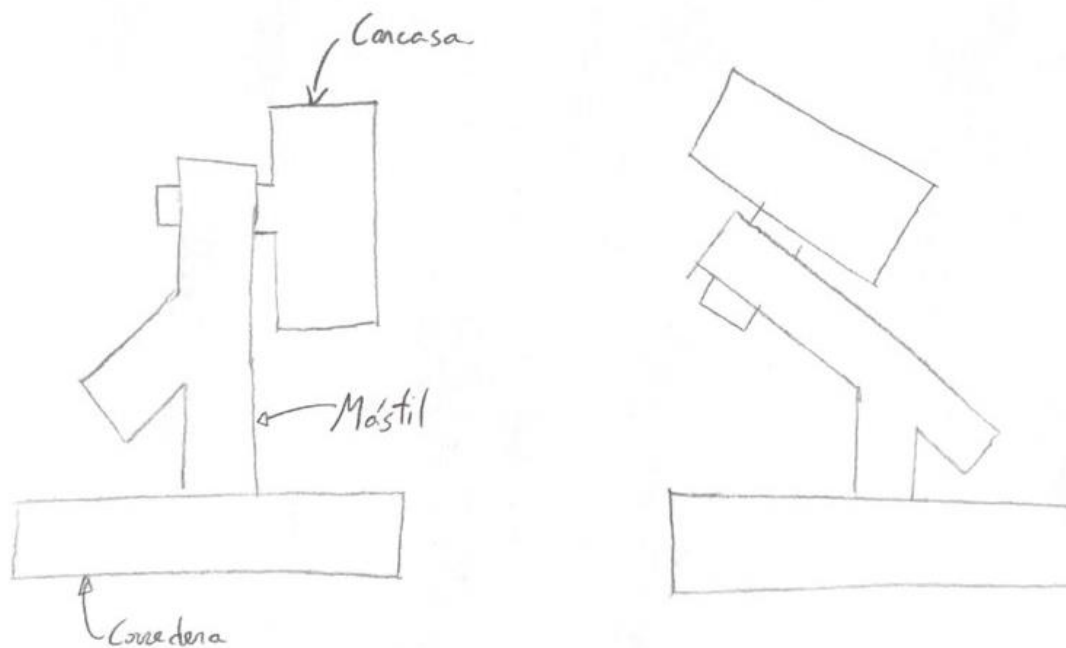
Vista lateral en la posición vertical (a la izquierda) y en la posición inclinado (a la derecha) del utillaje
